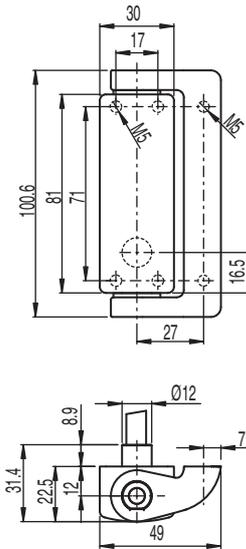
Dimensions du S400-M4-CB2PUR-W en mm
